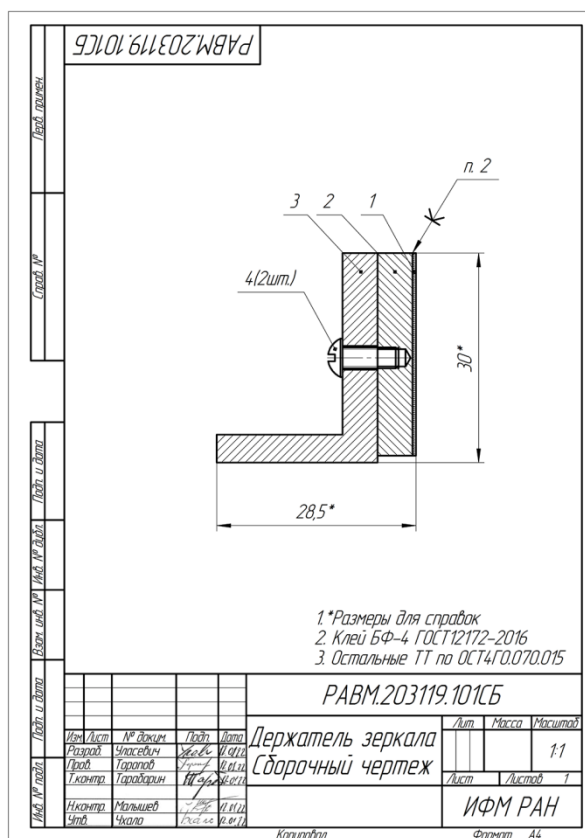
Сборочный чертёж держателя рентгеновского зеркала спектрометра МР и ЭУФ излучения
